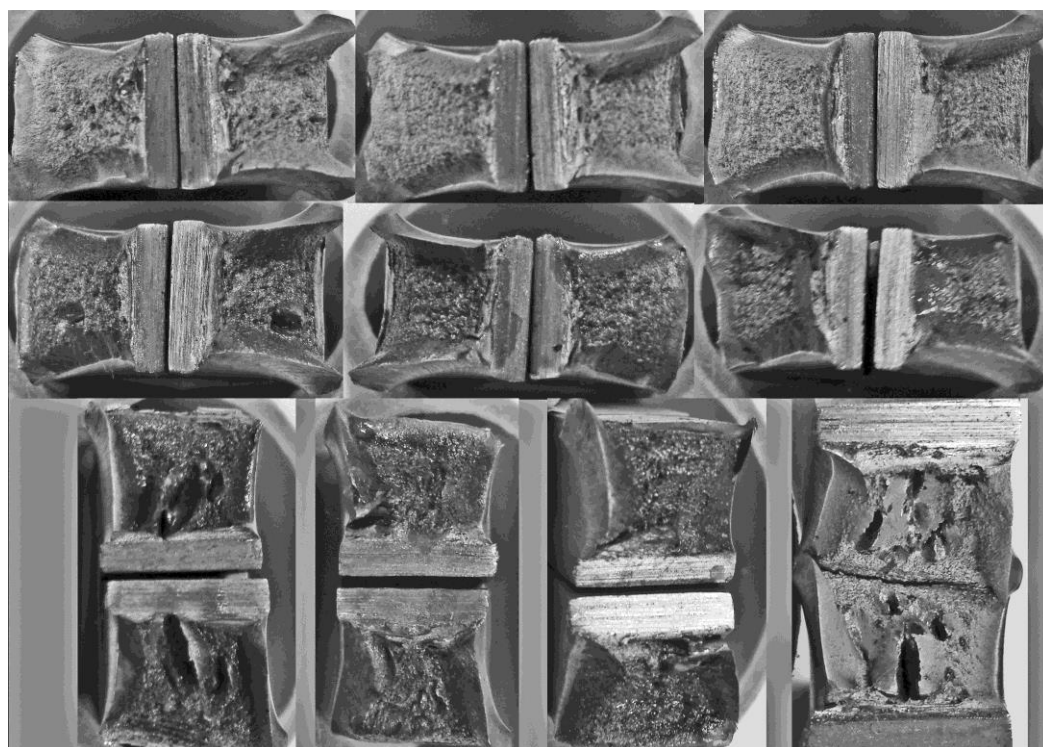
Fotografias das superfícies de fratura do ensaio Charpy-V, dos corpos de prova soldados com - 30 °C de pré-aquecimento.
